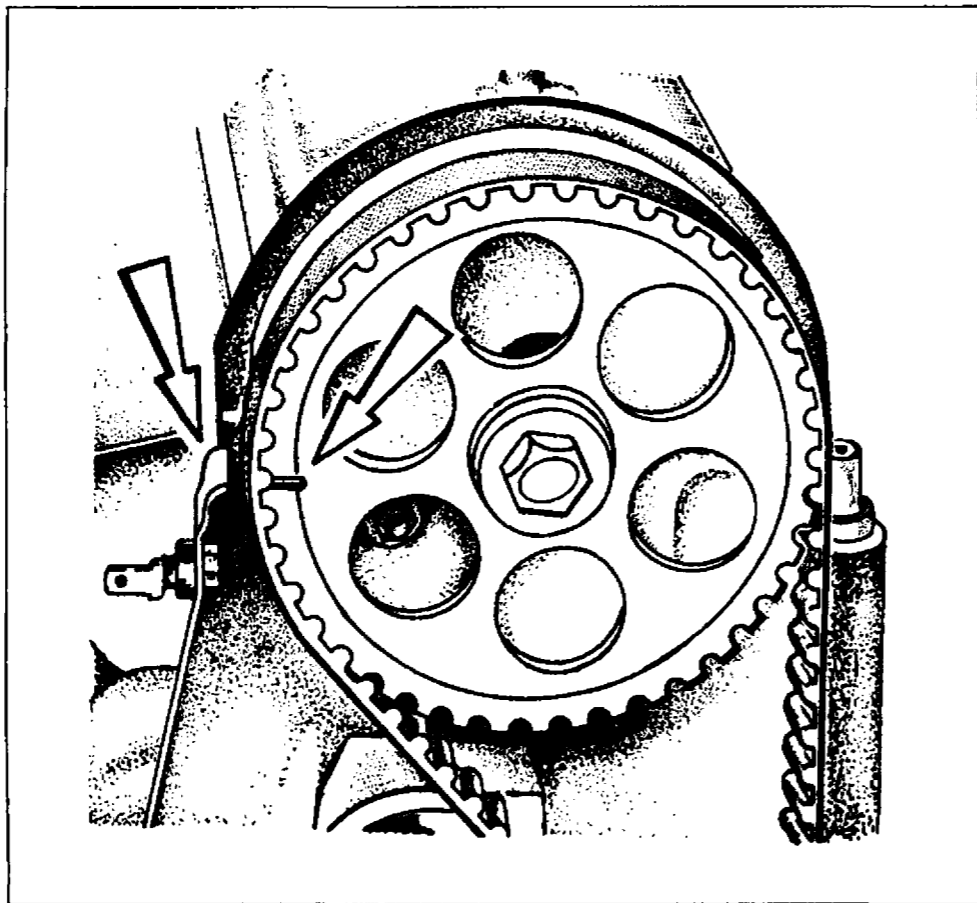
Проверка совпадения установочных меток на шкиве распределительного вала и задней защитной крышке
